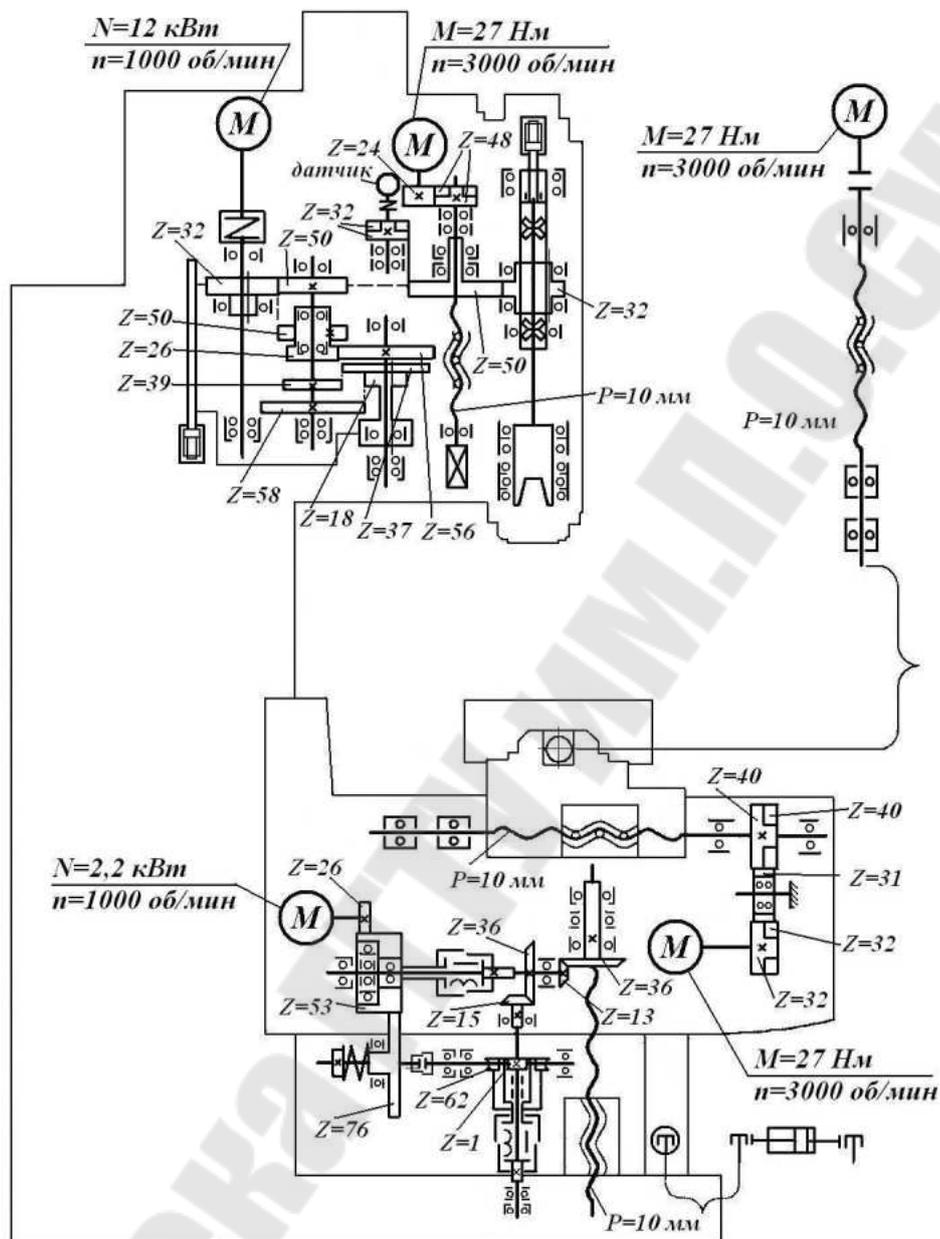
Схема кинематическая принципиальная станка с ЧПУ FSS400CNC
